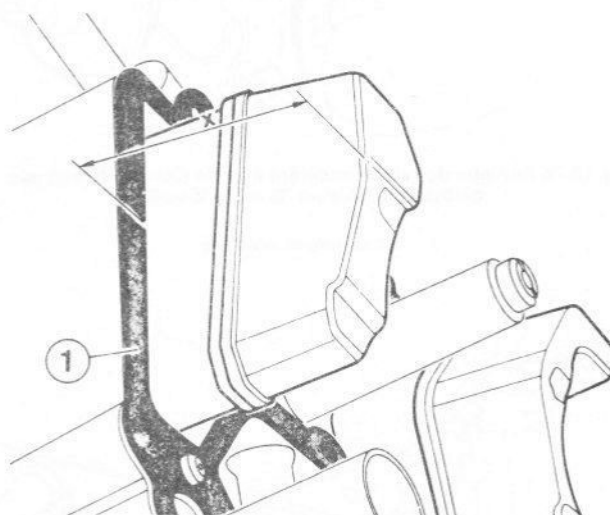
Réglage du niveau du flotteur - carburateur Weber 36 TLC (Sec 8)
